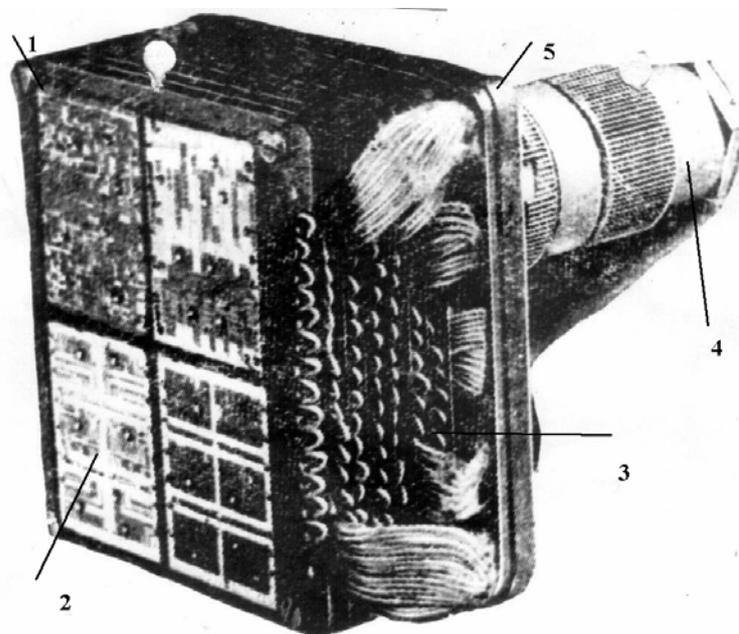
Этажерочная конструкция блока цифровой МЭА IV поколения: 1 - рамка; 2 - МСБ; 3 - межъячеечная коммутация; 4 - разъем; 5 - корпус со снятой крышкой
